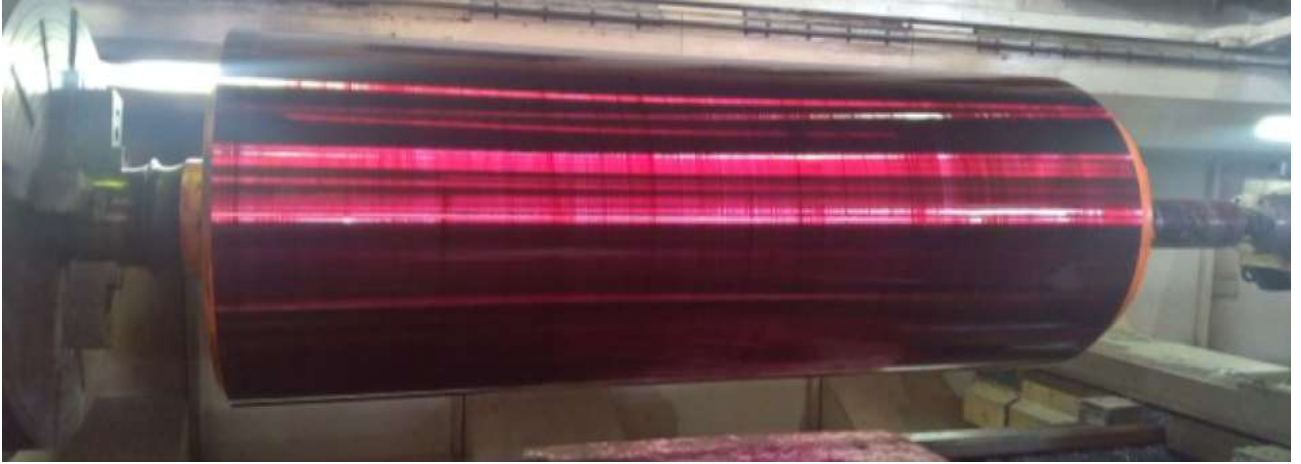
Rolo com penetrante após usinagem. Fonte: Autor
